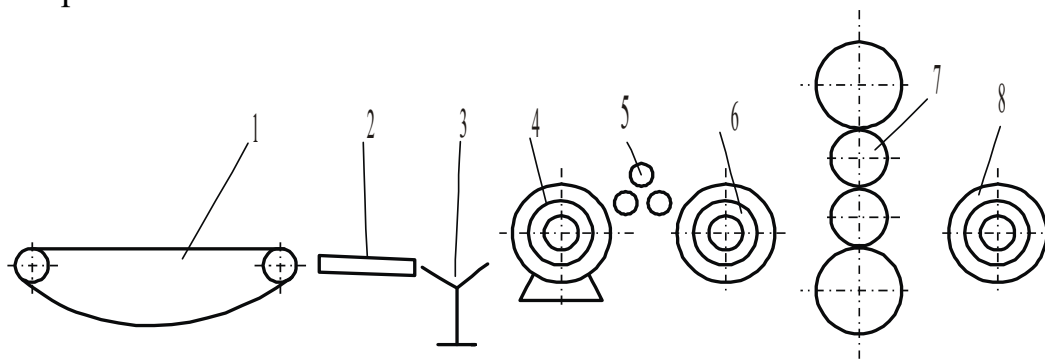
Схема реверсивного чотирьохвалкового стану холодної прокатки 1700
